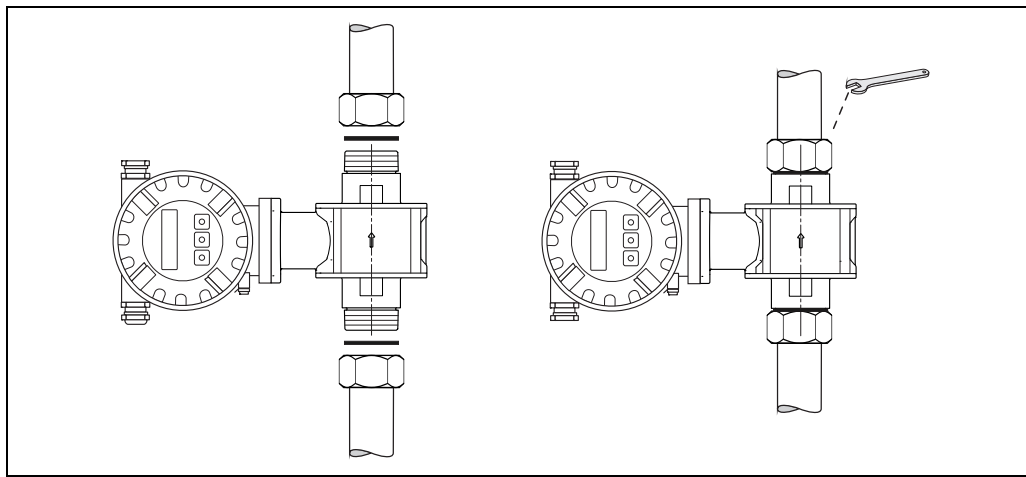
Instalação do sensor Promag D com conexão de rosca
